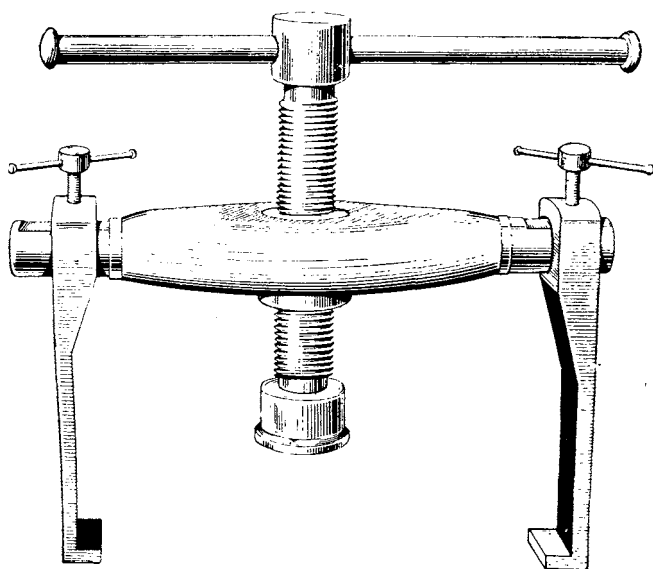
Съемник Э-240-П-002 сателлитов бортовой передачи
